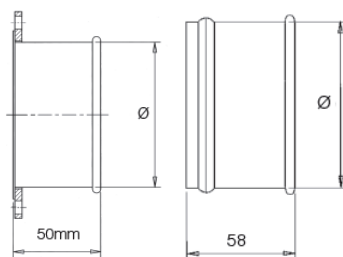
Adaptador para flange e mangueira, respetivamente (QFS Oil Mist & Cutting Fluid)
